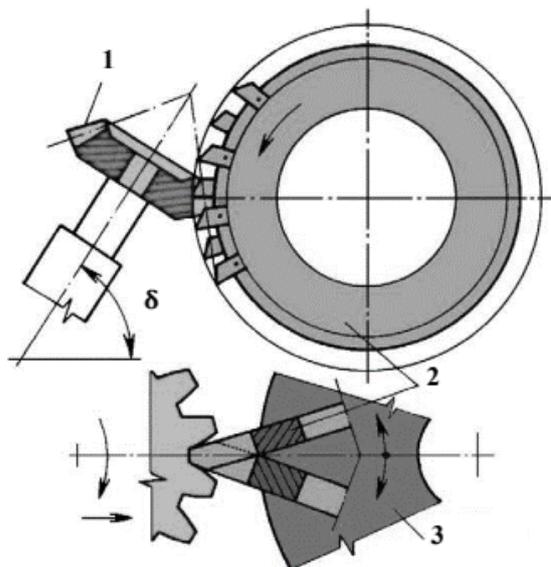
Frézování tvarovou kotoučovou frézou [12]
